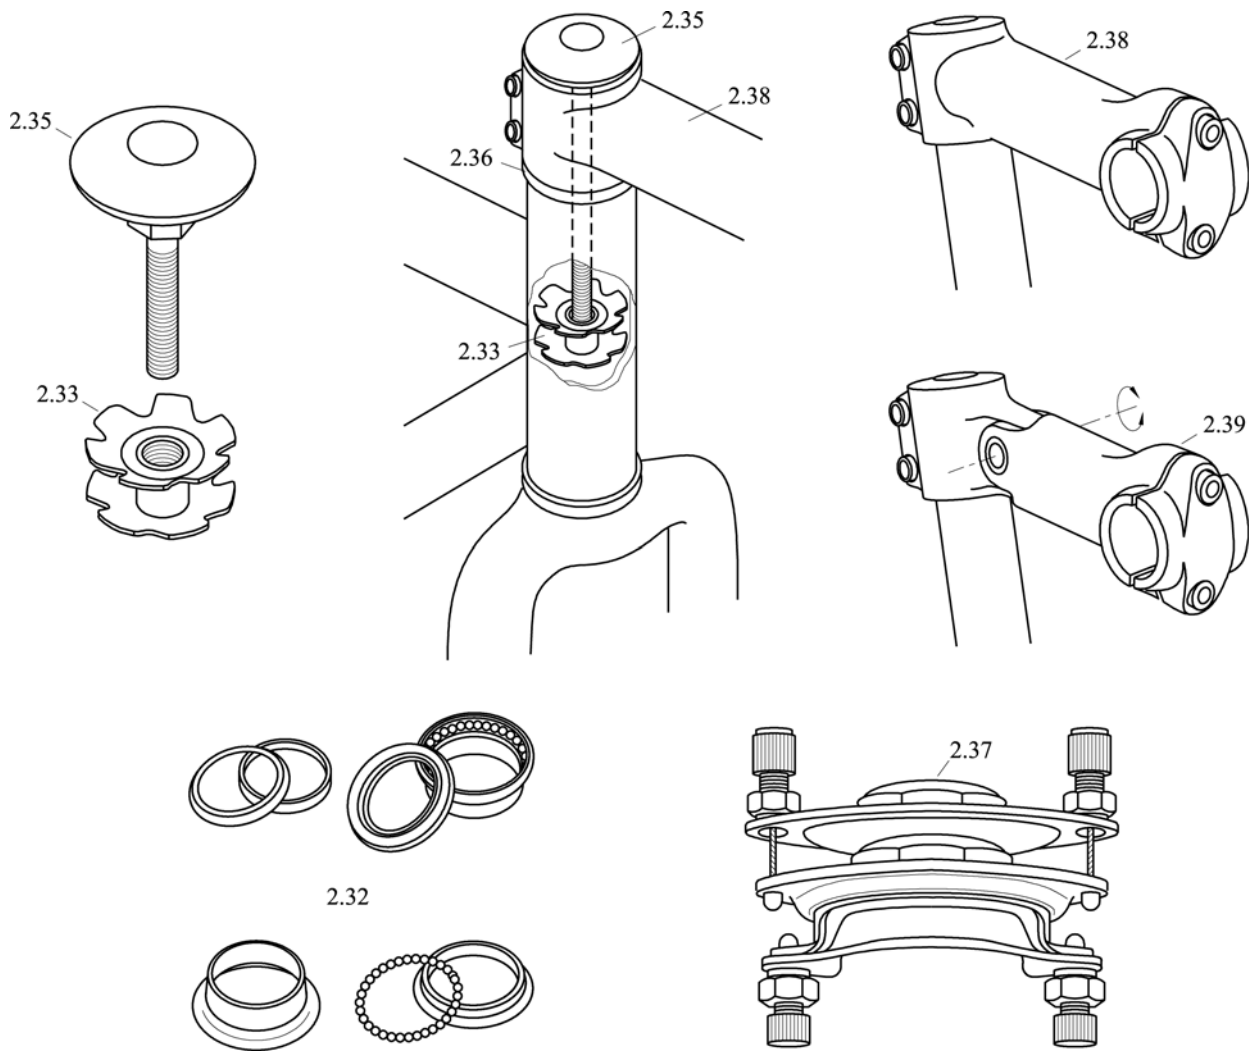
Ensemble de Direction / Head Assembly / Steuersatz und Lenkung / Gruppo sterzo / Balhoofd samenschooling
